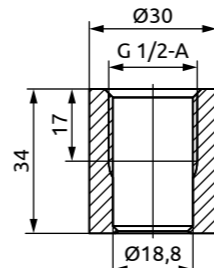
Габаритный чертеж приварного адаптера WA.22-G12-D30-SS6L
